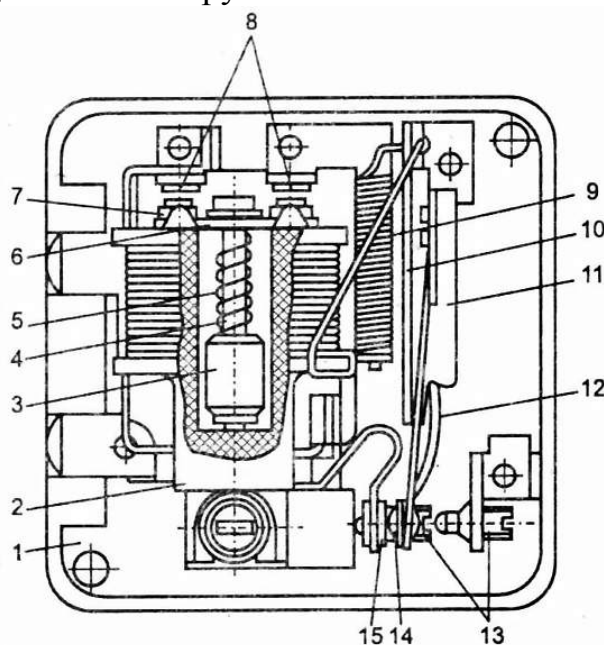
Реле РТК-Х: 1 – корпус; 2 – корпус котушки; 3 – сердечник; 4 – стрижень сердечника; 5 – пружина сердечника; 6 – планка; 7 – рухливі контакти пускового реле; 8 – нерухомі контакти пускового реле; 9 – нагрівач; 10 – біметалічна пластина; 11 – упор; 12 – контактотримач; 13 – регулювальні гвинти; 14 – рухливий контакт захисного реле; 15 – нерухливий контакт захисного реле
